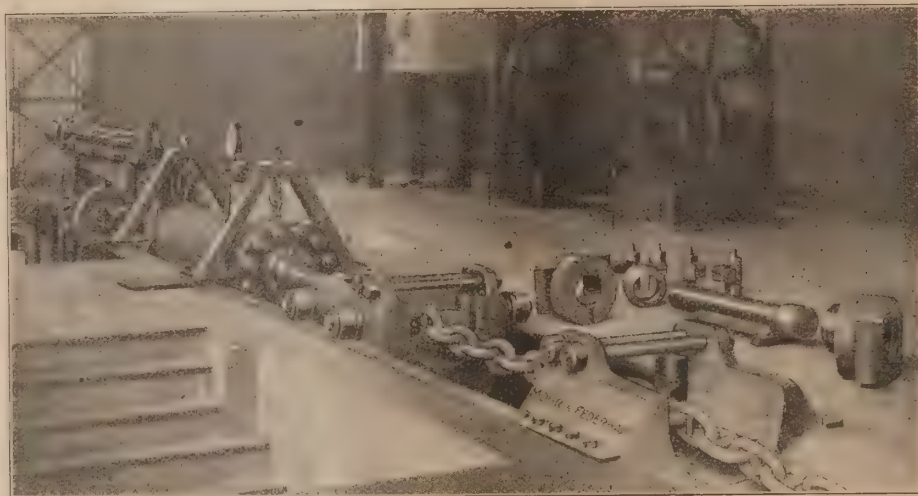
Kettenprüfmaschine von 300 t Zugkraft mit Laufgewichtswage.
